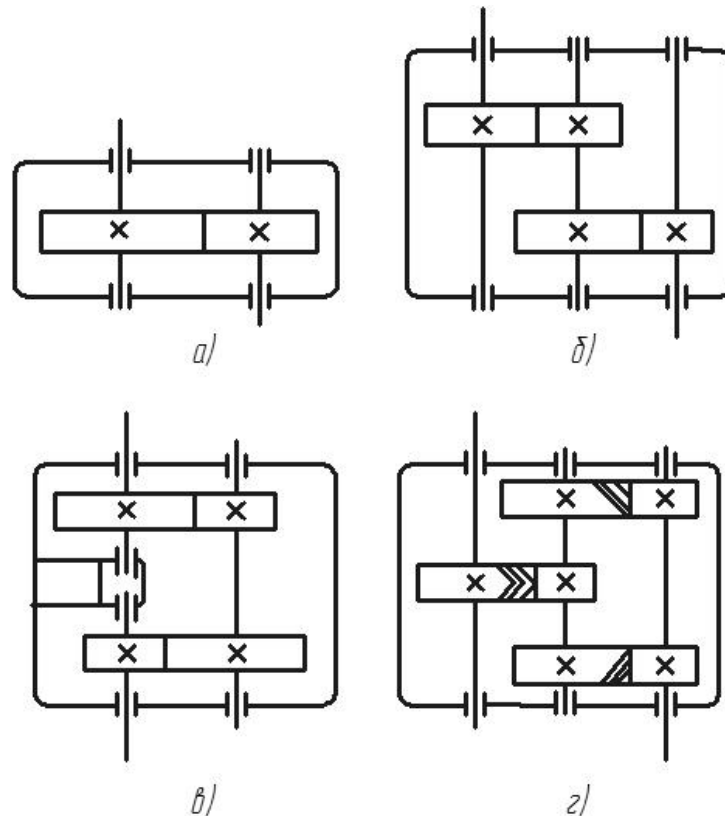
Принципові схеми циліндричних зубчастих редукторів
